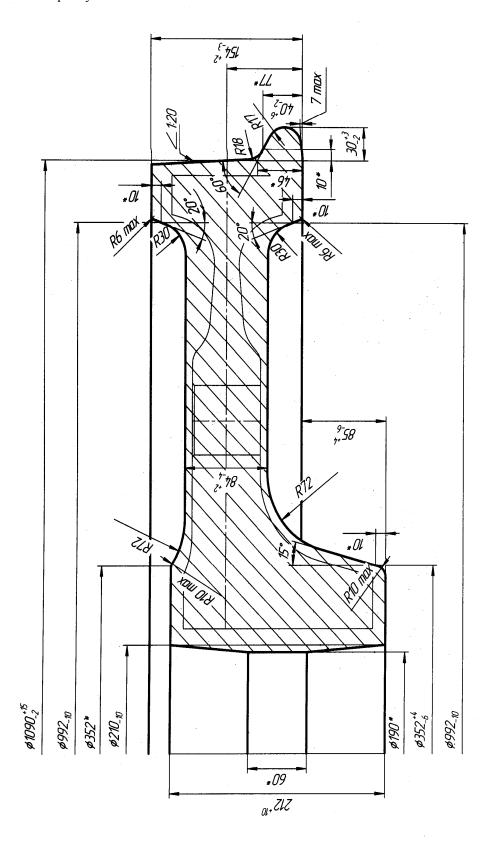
Заготовка черновая Ø 1090 мм (под чистовой центр колесный Ø 1070,6 мм чертеж № КР-0079-09/ТЭП70А.31.15.119)
